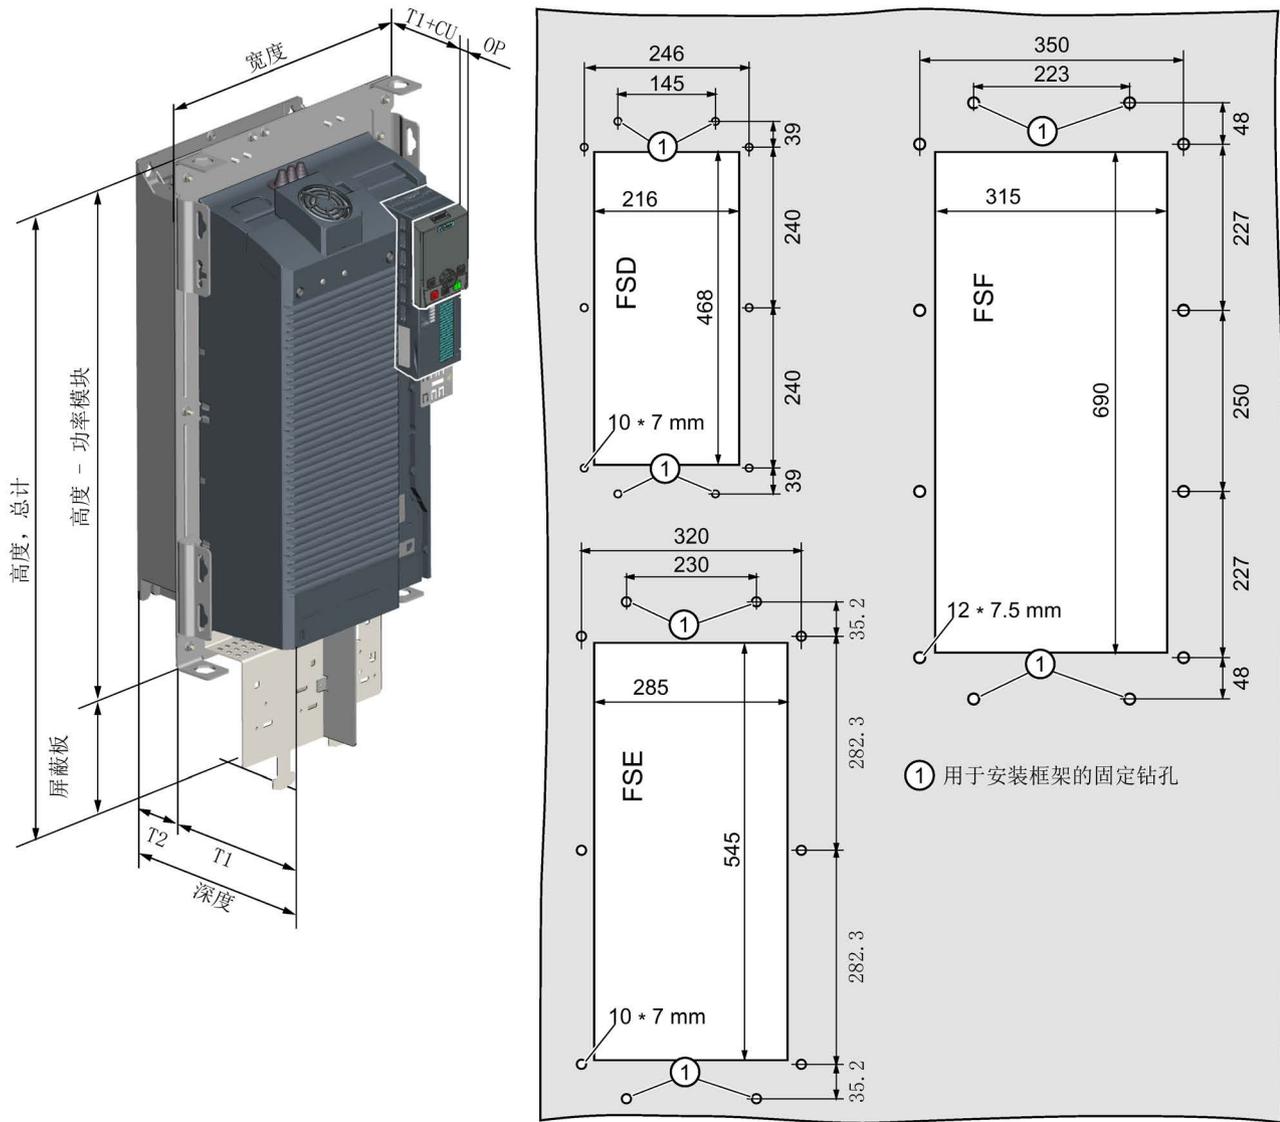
FSD ... FSF 型的尺寸图和钻孔图
